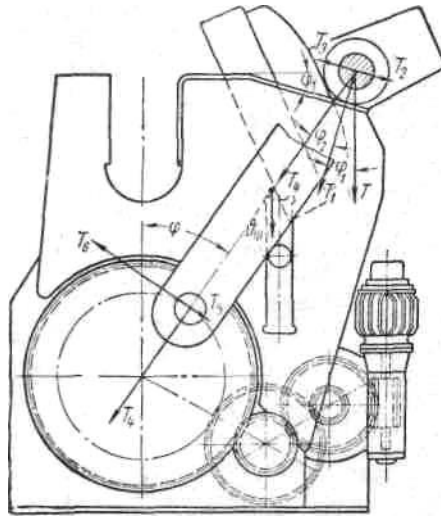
Розрахункова схема приводу форматора-вулканізатора 55"
